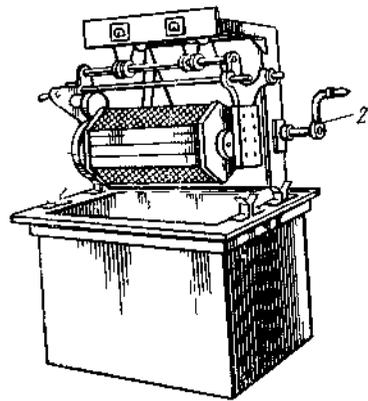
Ванна барабанного типа для гальванических покрытий: 1 — барабан, 2 — подъемный механизм
